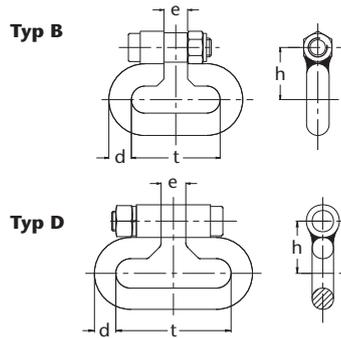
Kettenschloss Typ B mit angeschweißter Mutter, Typ D mit loser Mutter
